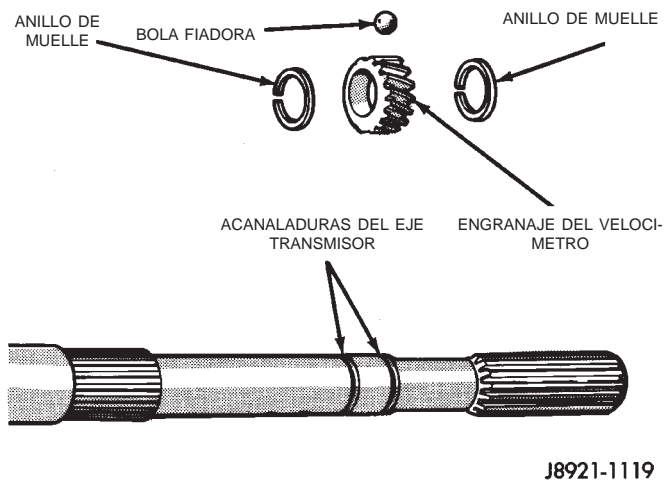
Conjunto del engranaje propulsor del velocímetro
